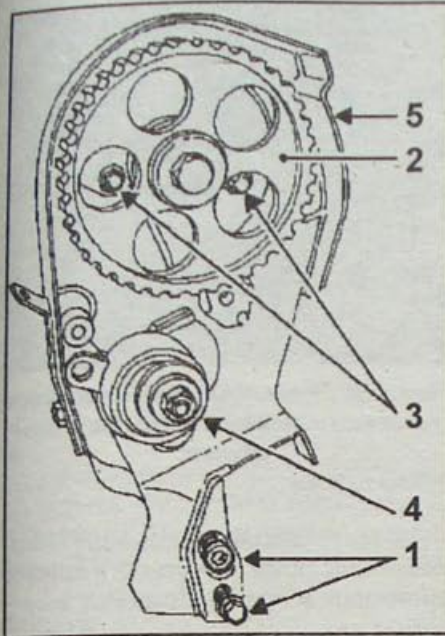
Расположение болтов (3) крепления верхнего внутреннего кожуха (5), болтов (1) крепления внутреннего кожуха, шкива распределительного вала (2) и натяжного устройства газораспределительно-го механизма (4)
